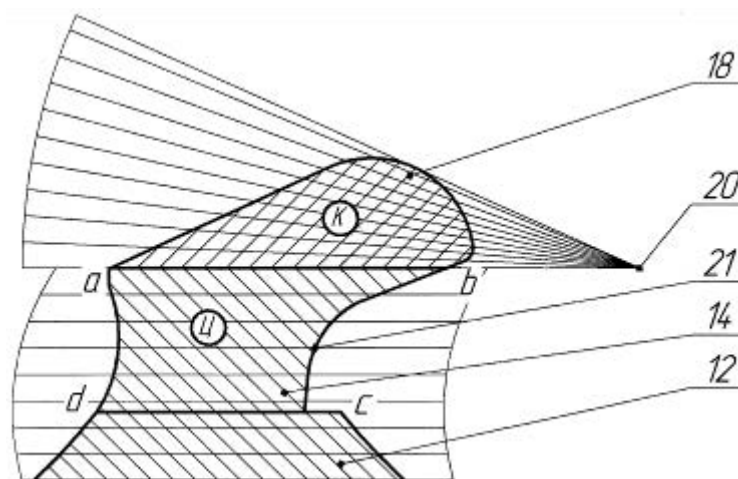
Схема развертывающейся комбинированной лемешно-отвальной поверхности корпуса
